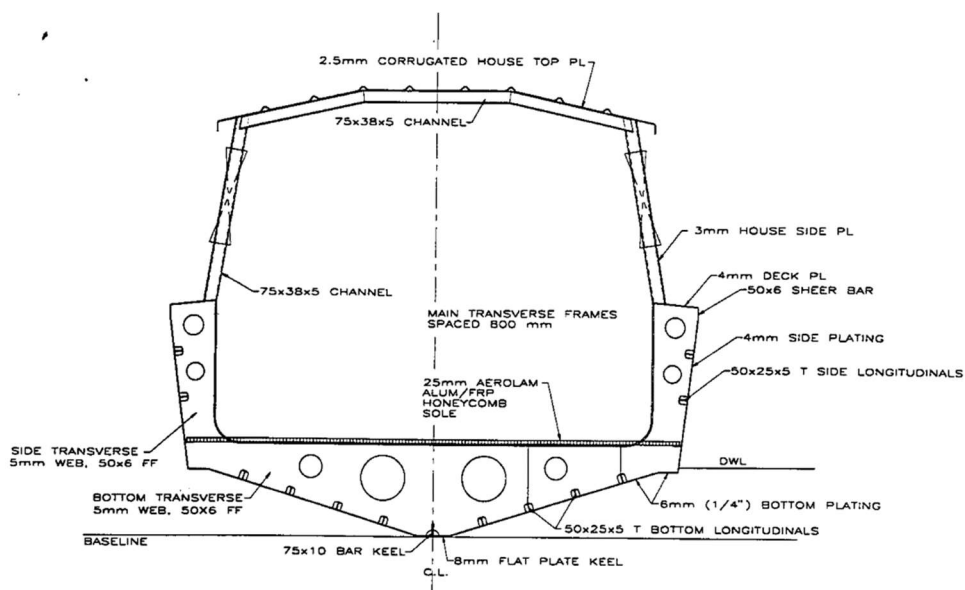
Visão dos elementos estruturais da seção mestra da embarcação original (fonte: autor)
